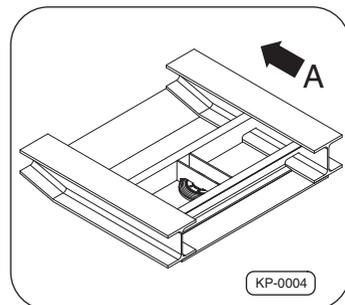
· Beispiel für Einbaulage in Fahrtrichtung
